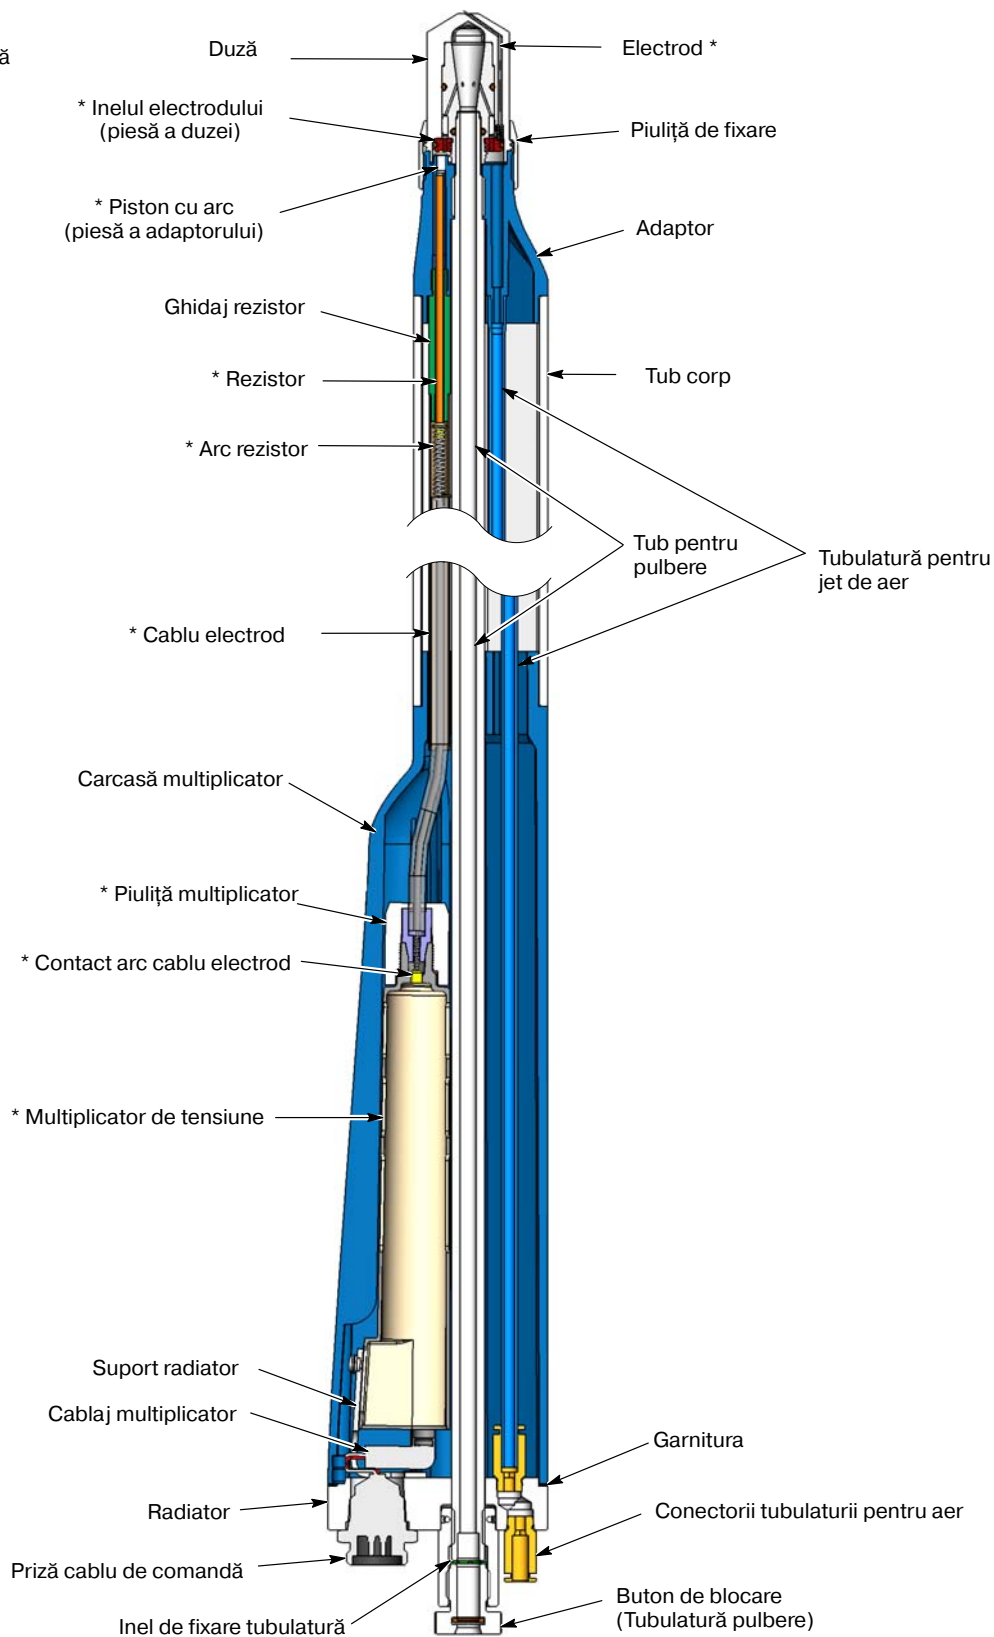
Vedere în secțiune - Componentele și ansamblul pistolului montat pe tub
